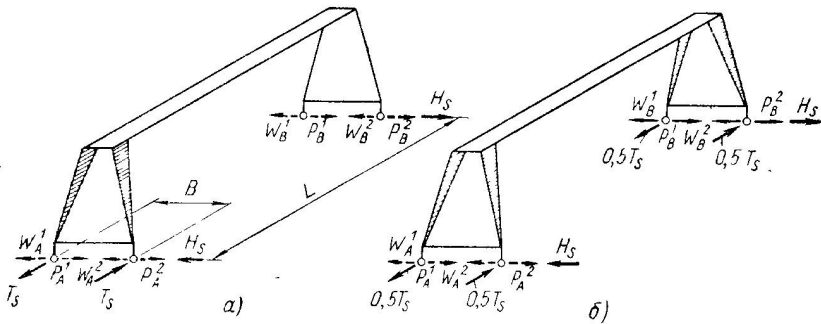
Схеми навантажень, що діють при перекосі:
